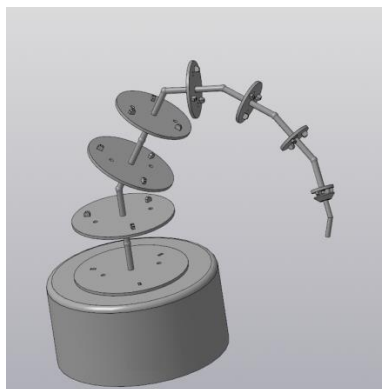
Сварочный робот на базе гибкого манипулятора
